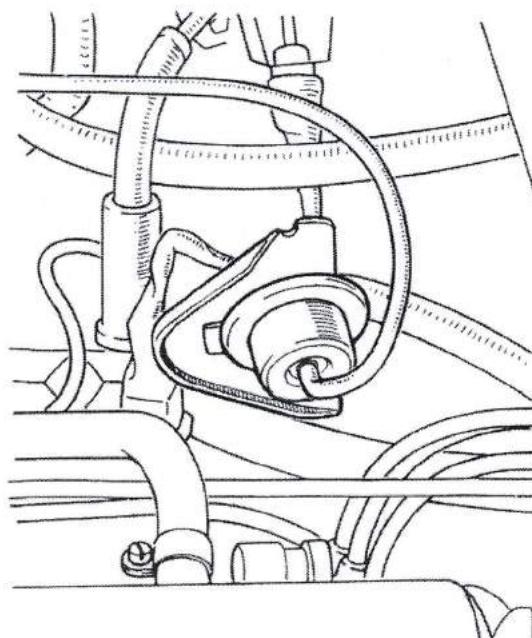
Disposición del regulador de presión instalado en el extremo de la rampa de inyección.
